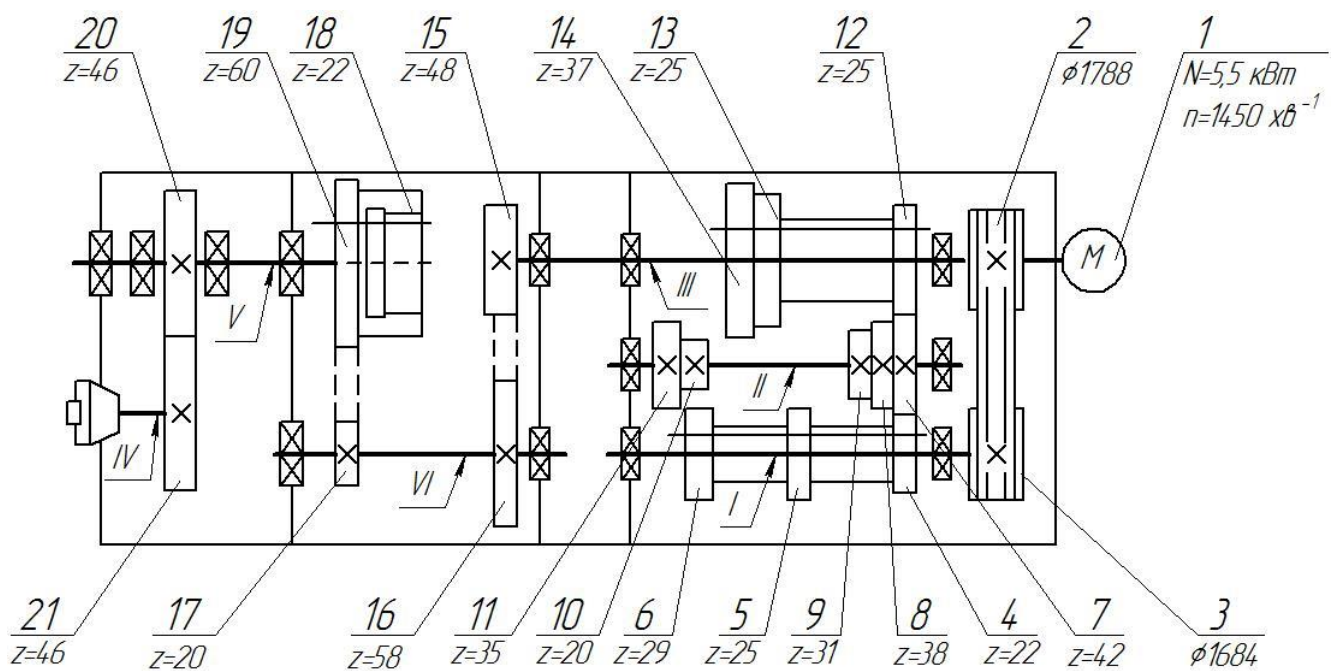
Принципова кінематична схема привода головного руху
